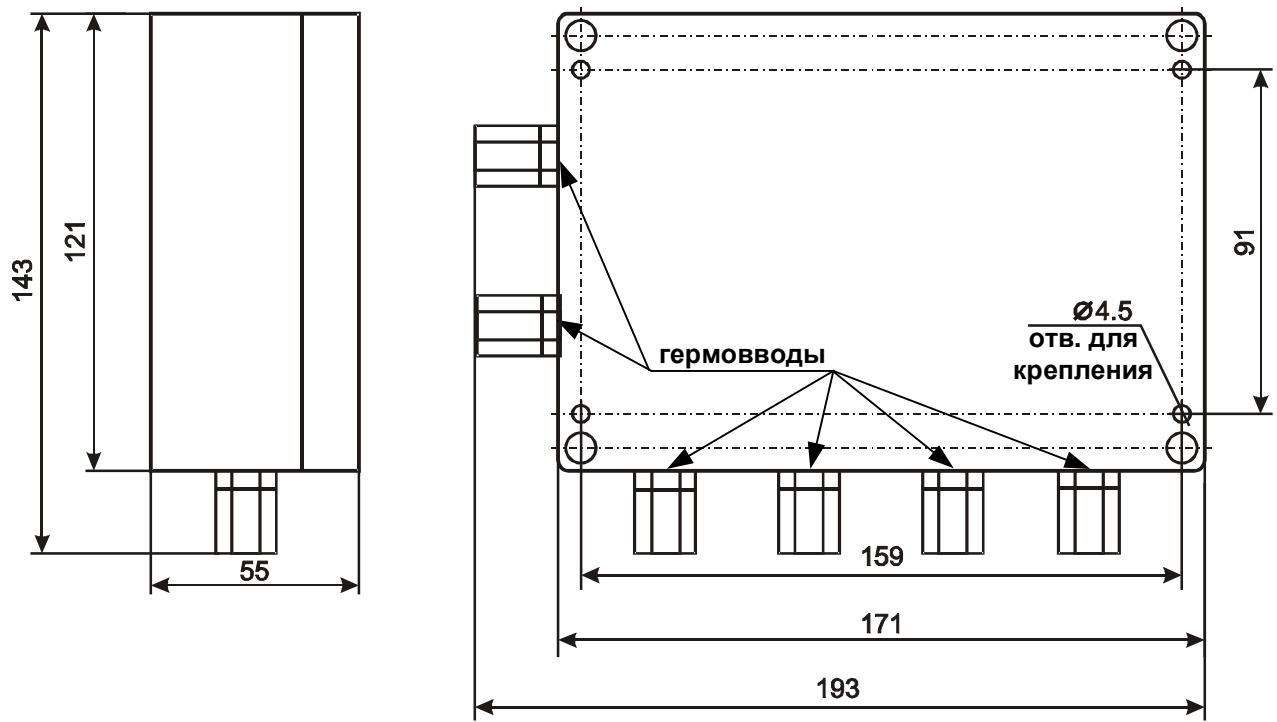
Внешний вид и габаритные размеры СКИУ исп. IP65, "К"
